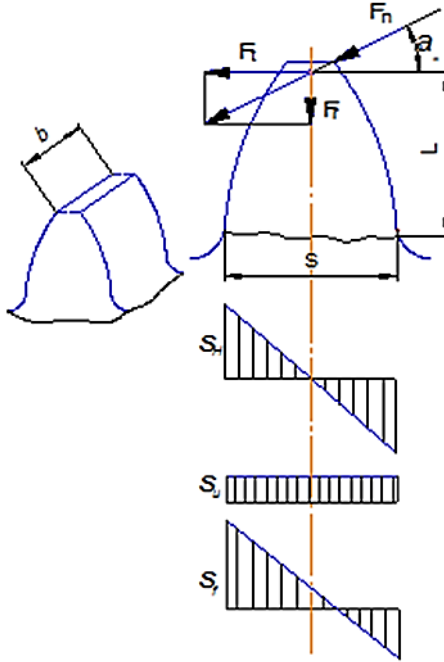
Расчетная схема нагружения зуба прямозубого цилиндрического колеса
